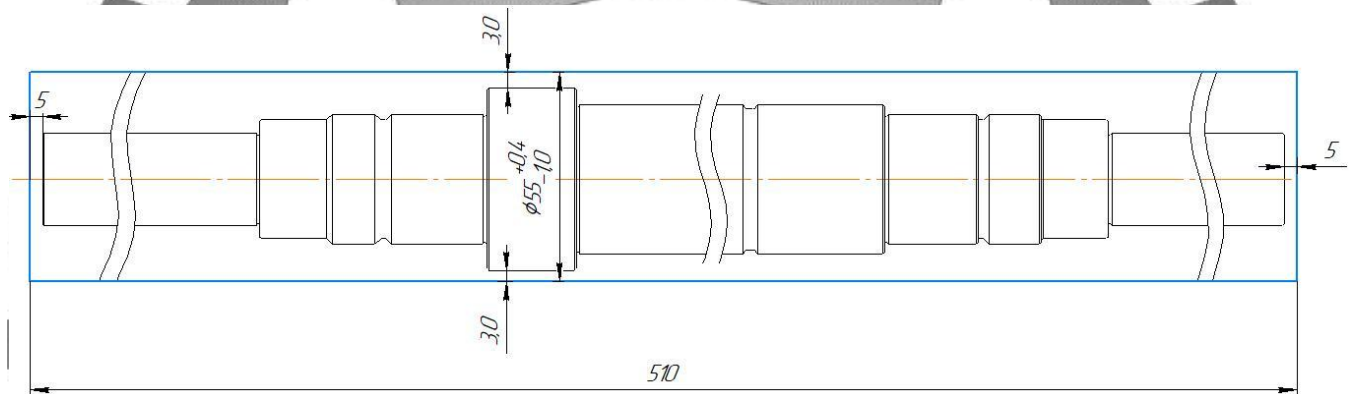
Заготовка, яка виготовлена із круглого прокату
